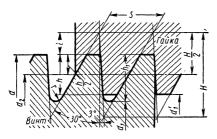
Профиль упорной резьбы по ГОСТУ 10177—62: H=1,5878 S; $h_1=0,68777$ S; i=0,4189 S; r=0,12427 S; h=0,75 S; $(d_2=d-h; d_1=d-2h; d_1=d-2h)$
